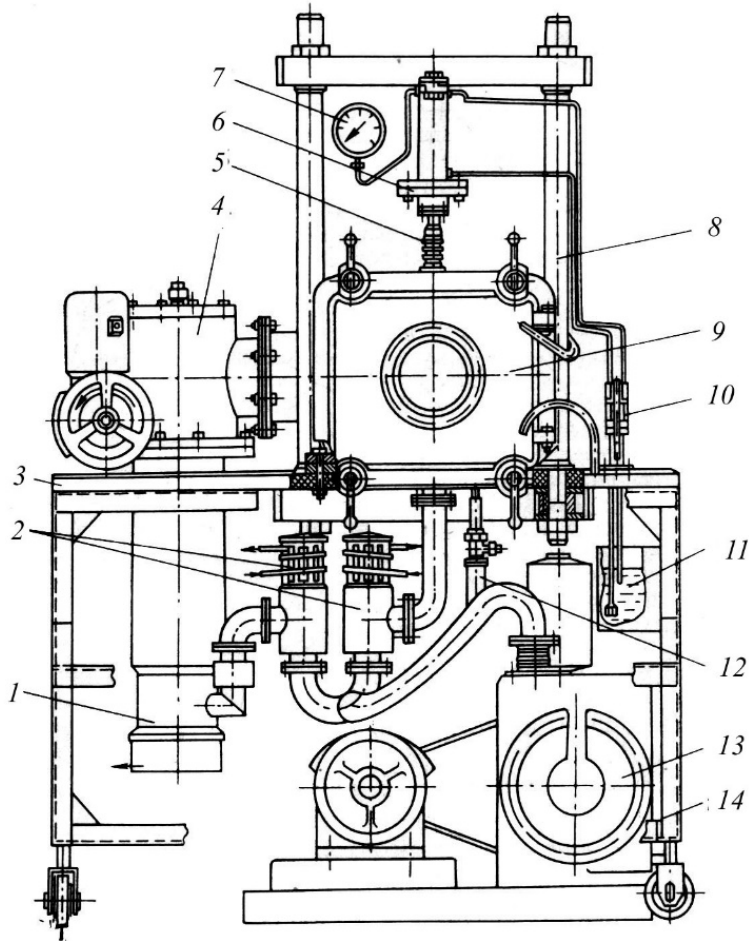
Схема вакуумної установки УДСВ-ДТ для дифузійного зварювання деталей лопаток газових турбін
